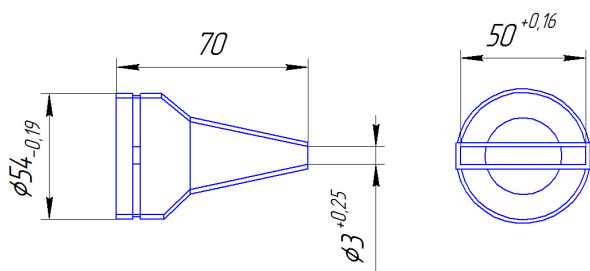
Специализированная насадка для локального нагрева медной пластины коллектора тягового электродвигателя ТЛ-2К1
